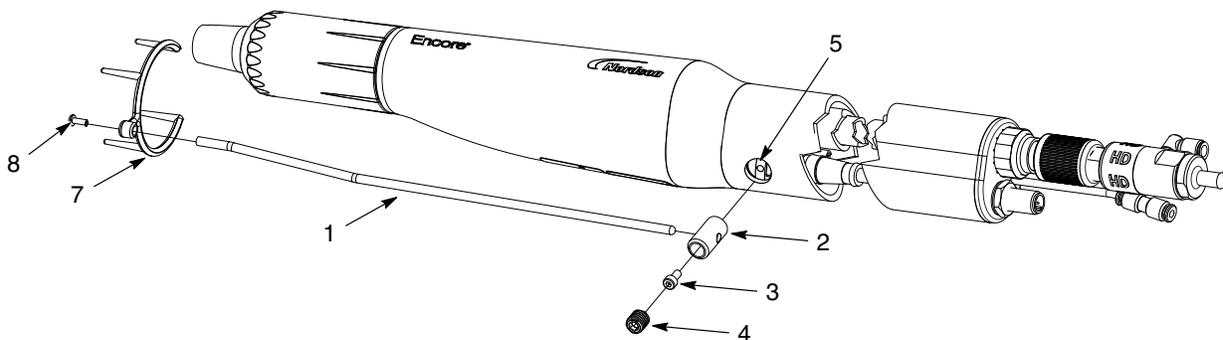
Instalação do coletor de iões - pistola com tubo de suporte
